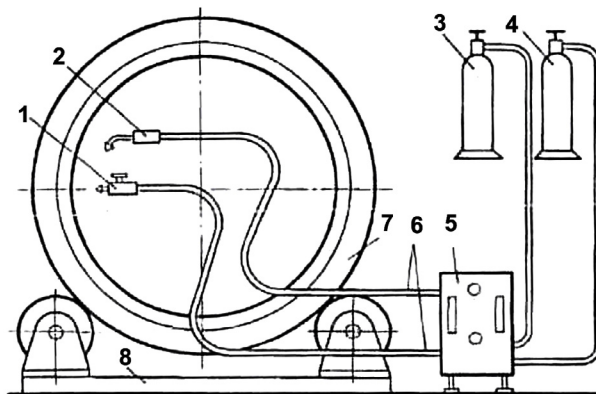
Схема газопламенного напыления уплотнительного кольца:
